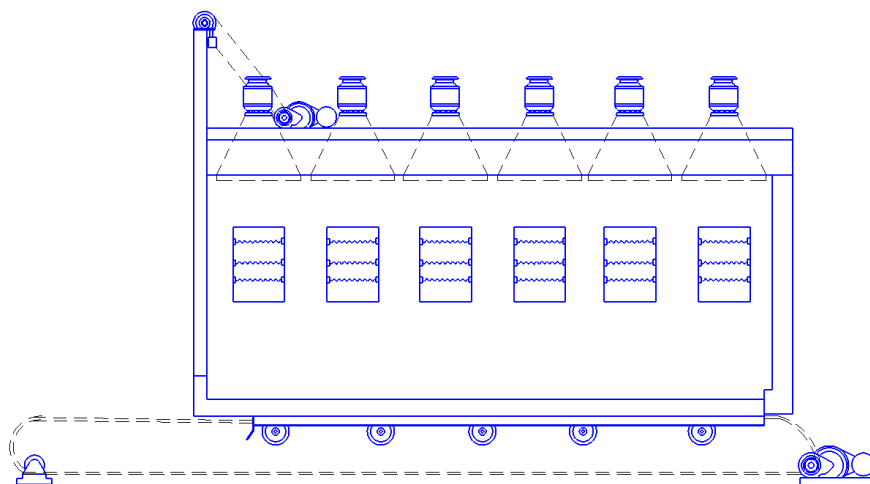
Камерная электропечь для отпуска сварных конструкций
